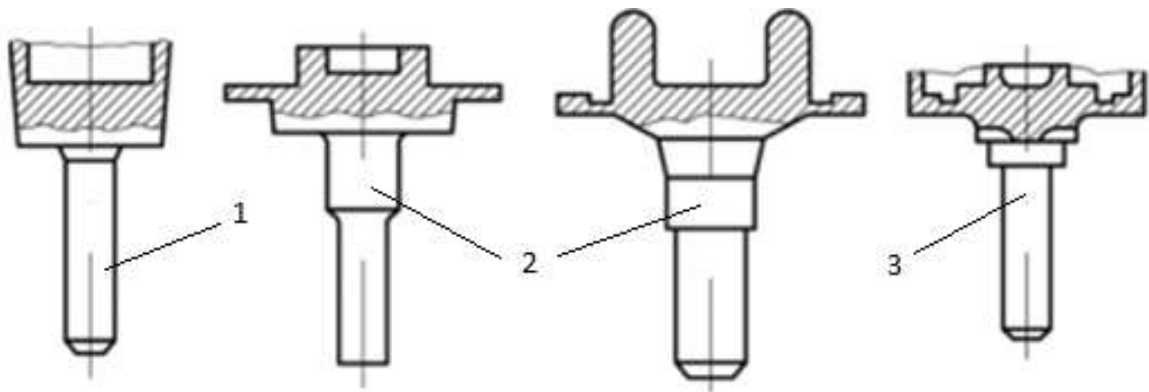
Конструкцій заготовок після штампування витискуванням:
